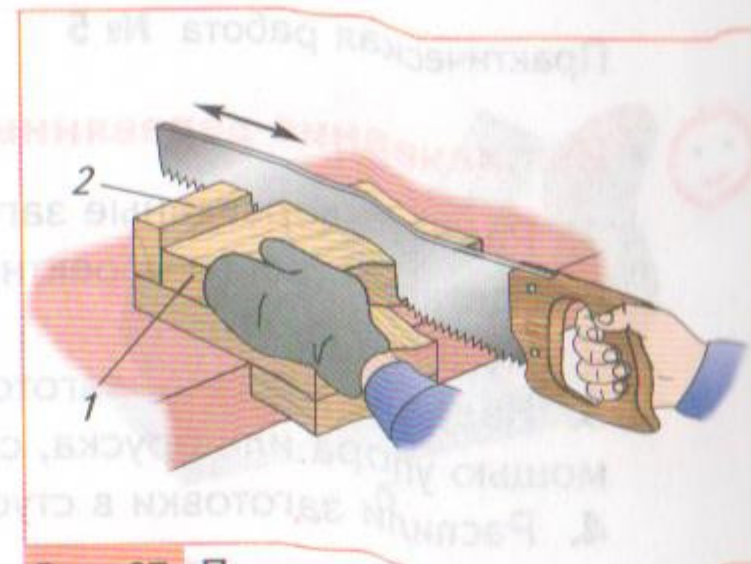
Пиление с упором: 1 — заготовка; 2 — упор
